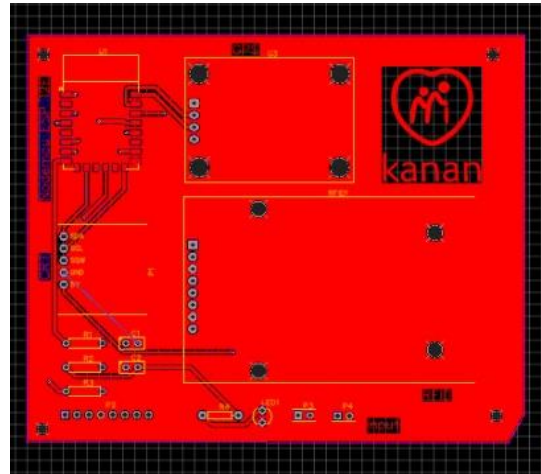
Diseño de Placa de Circuito Impreso (PCB)
